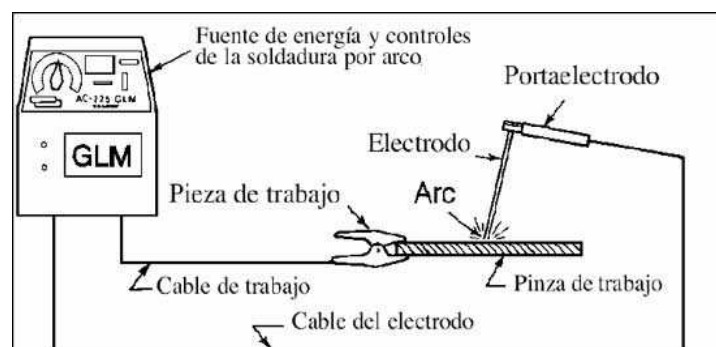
Proceso de Soldadura Eléctrica
